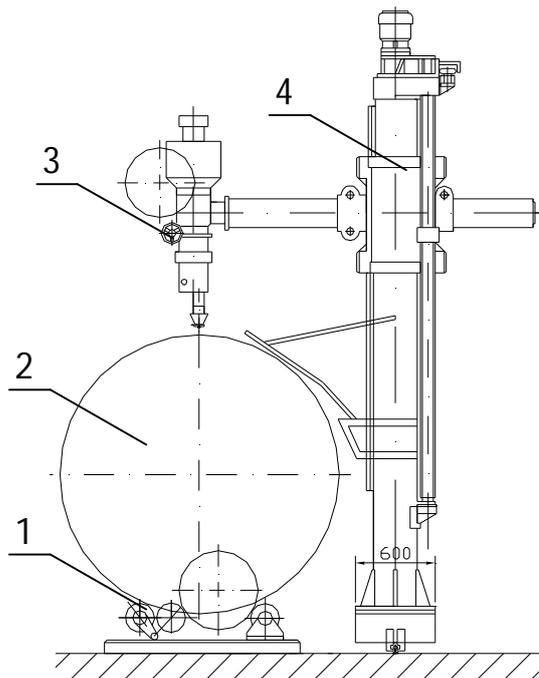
Установка для сварки кольцевых швов корпуса
